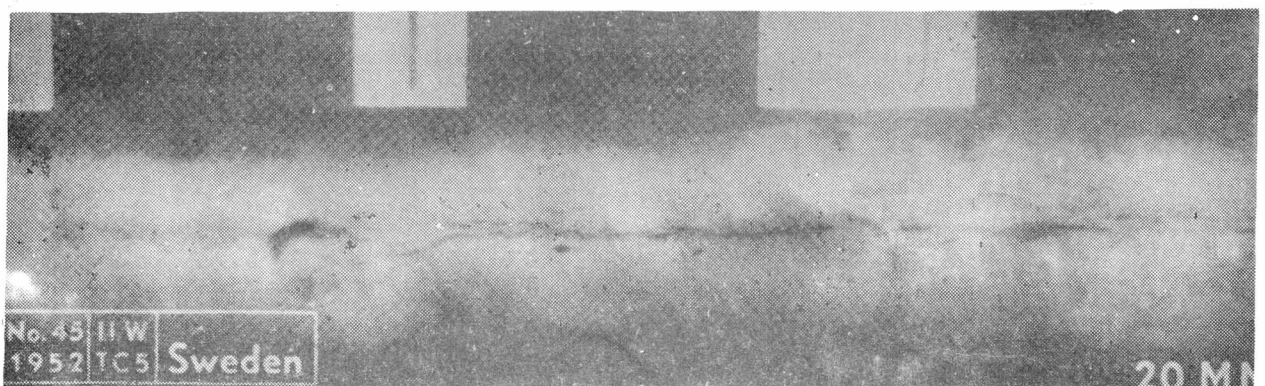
Algunos defectos e inclusiones en soldaduras.
